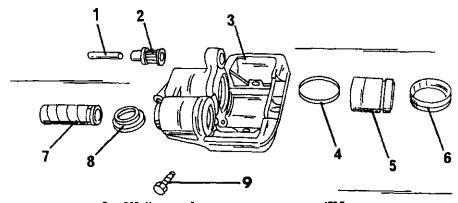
Монтажный чертеж тормозного суппорта ATE Teves.
